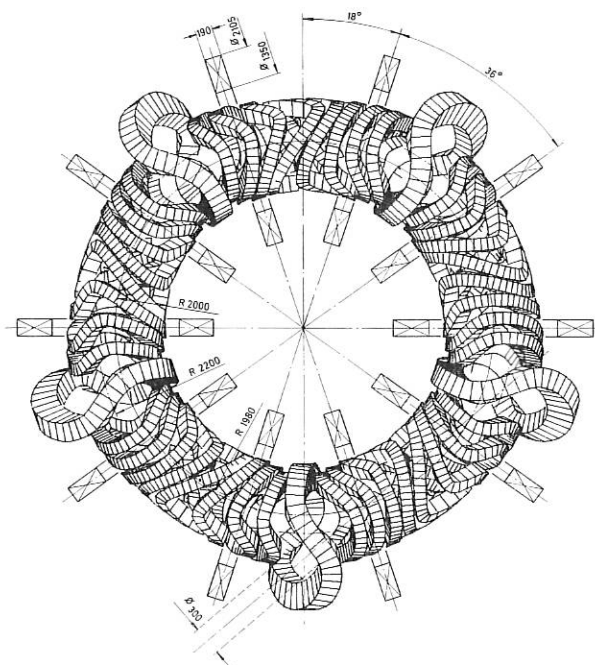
Draufsicht und Schnitt der Spulen für die Einschlußfelder.
